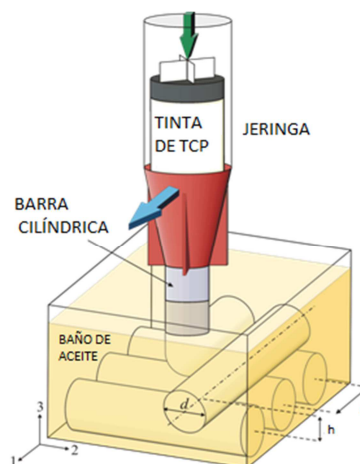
Esquema del proceso de impresión en tres dimensiones.
